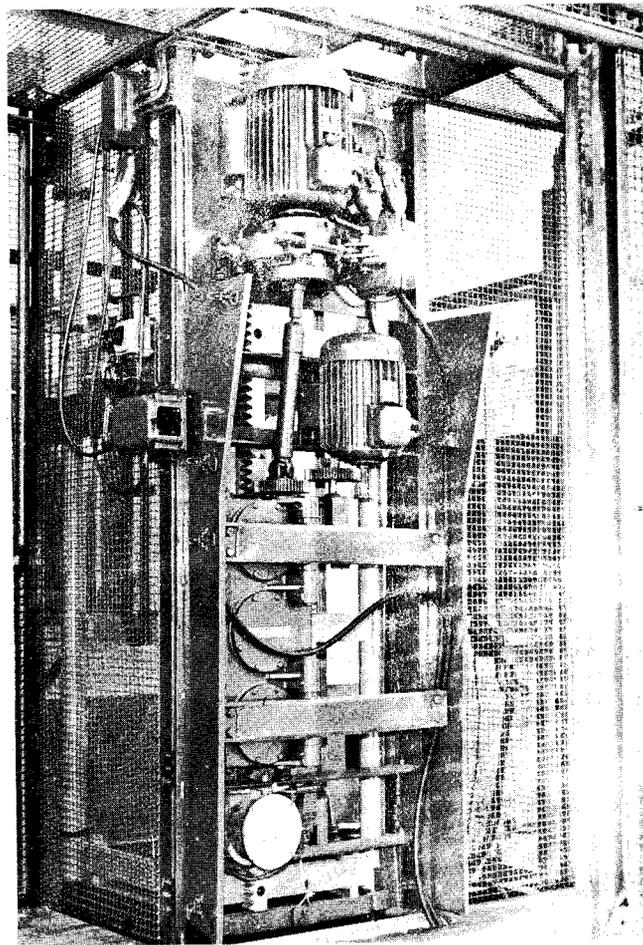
Vista ilustrando una máquina de engranaje cilíndrico de dentadura recta, nótese esto último en el medio interior de la figura.
